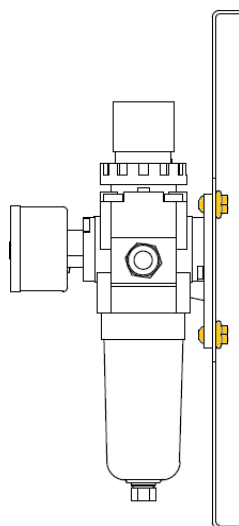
Монтаж крепежной пластины на блок подготовки воздуха
